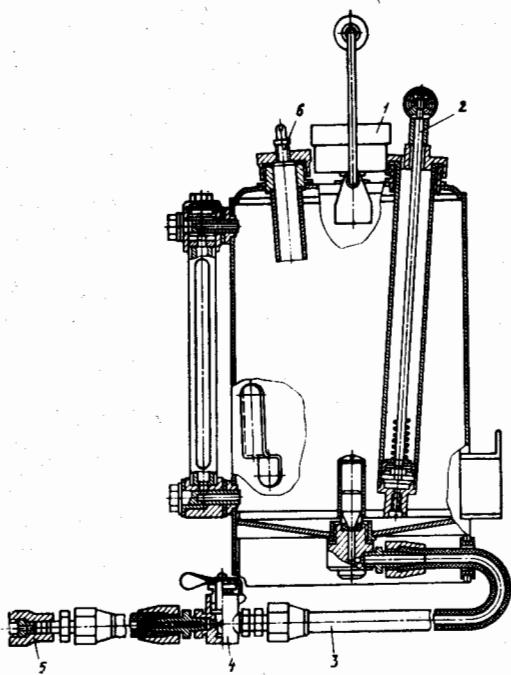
Прибор для проверки герметичности системы питания двигателя топливом:
